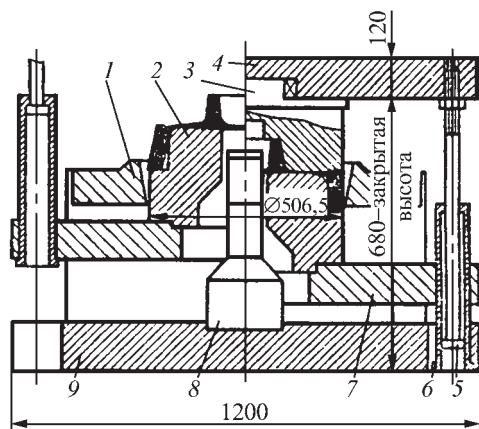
Совмещенный штамп для одновременной обрезки, пробивки, правки и обжима:
